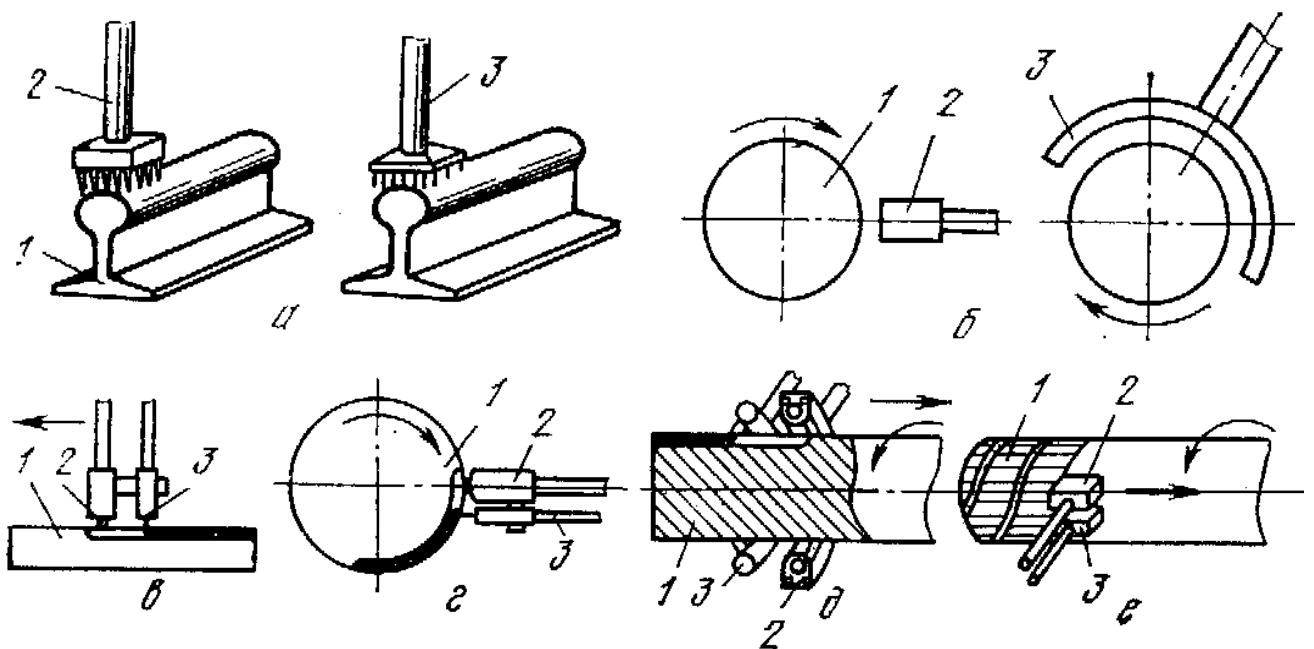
Способи поверхневого гартування деталей за допомогою зовнішніх джерел тепла:
